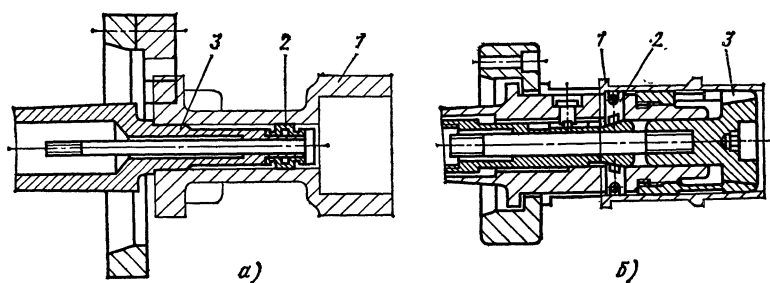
Оправки с комбинированными центрирующими зажимными механизмами для одно-временной установки заготовки 1:
